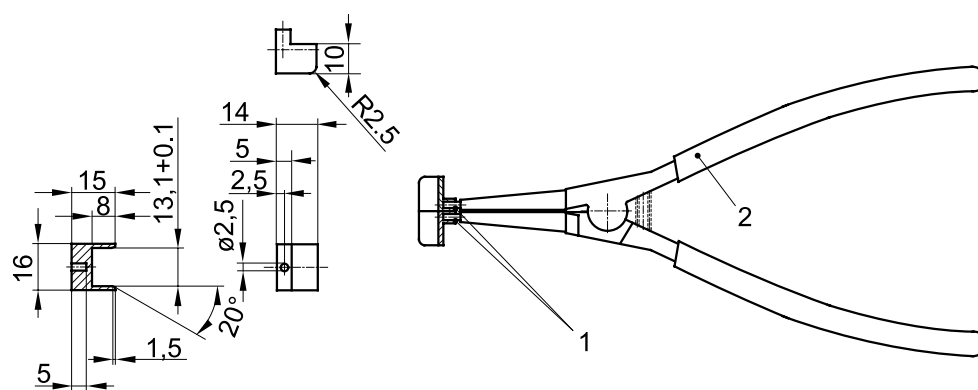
Werkzeug zum Lösen der Kabelstecker für den Temperatursensor vom Kabelbaum
